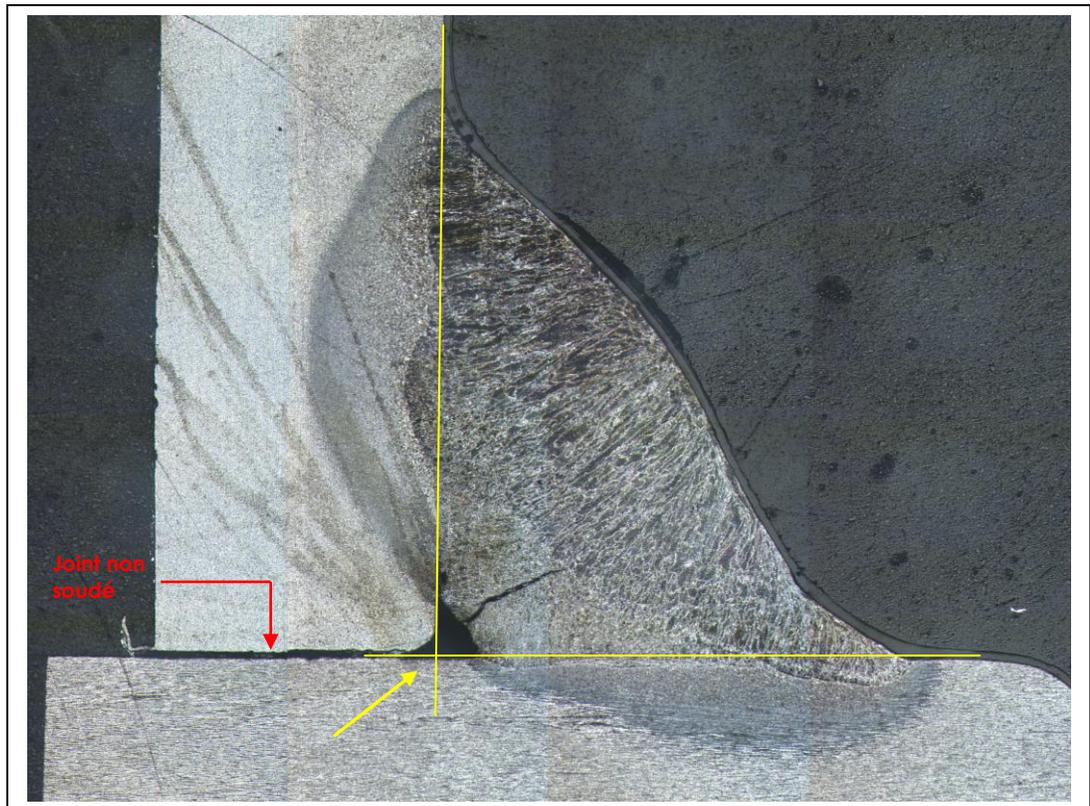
Fissure à la racine du cordon de soudure 2DE - surface ext.
